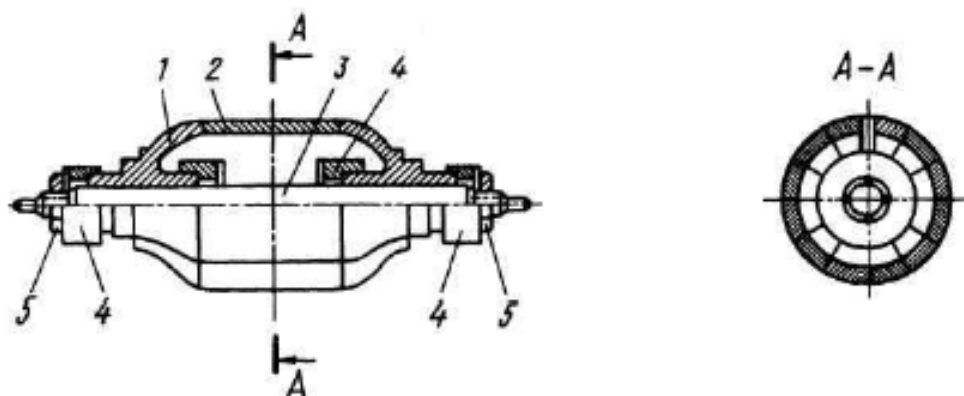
Конструктивная схема металлической оправки: 1 - разборные части оправки, формирующие днища сосудов; 2 - цилиндрическая часть оправки; 3 - вал; 4 - гайки для сборки частей днищ; 5 - гайки крепления оправки на валу
